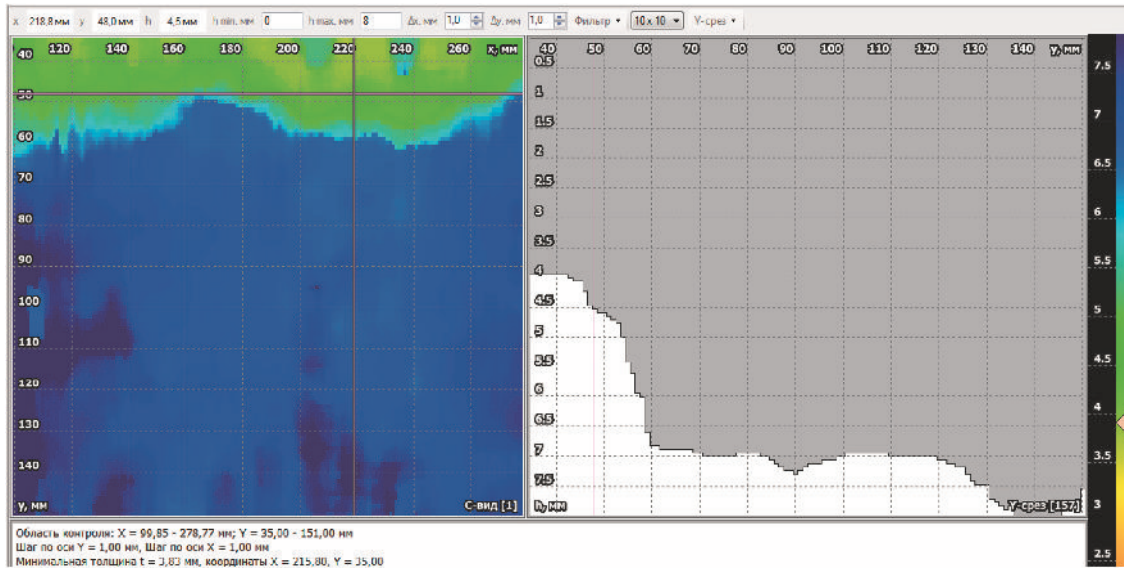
Карта толщины образца с реальным ЭКИ в области основного металла
